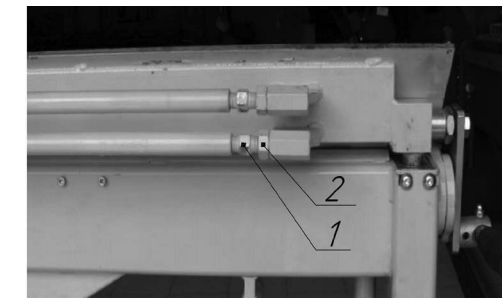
Регулировка поперечного прогиба прижимной балки станка Metal Master LBM 250
